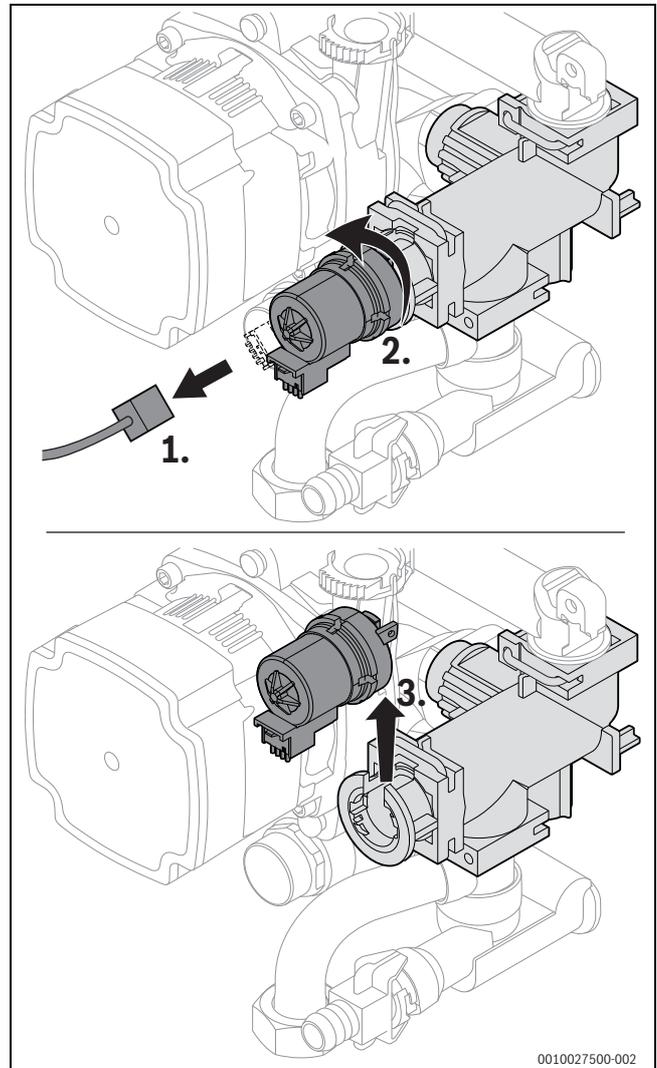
Motor am 3-Wege-Ventil ausbauen (Variante ohne Schrauben)
